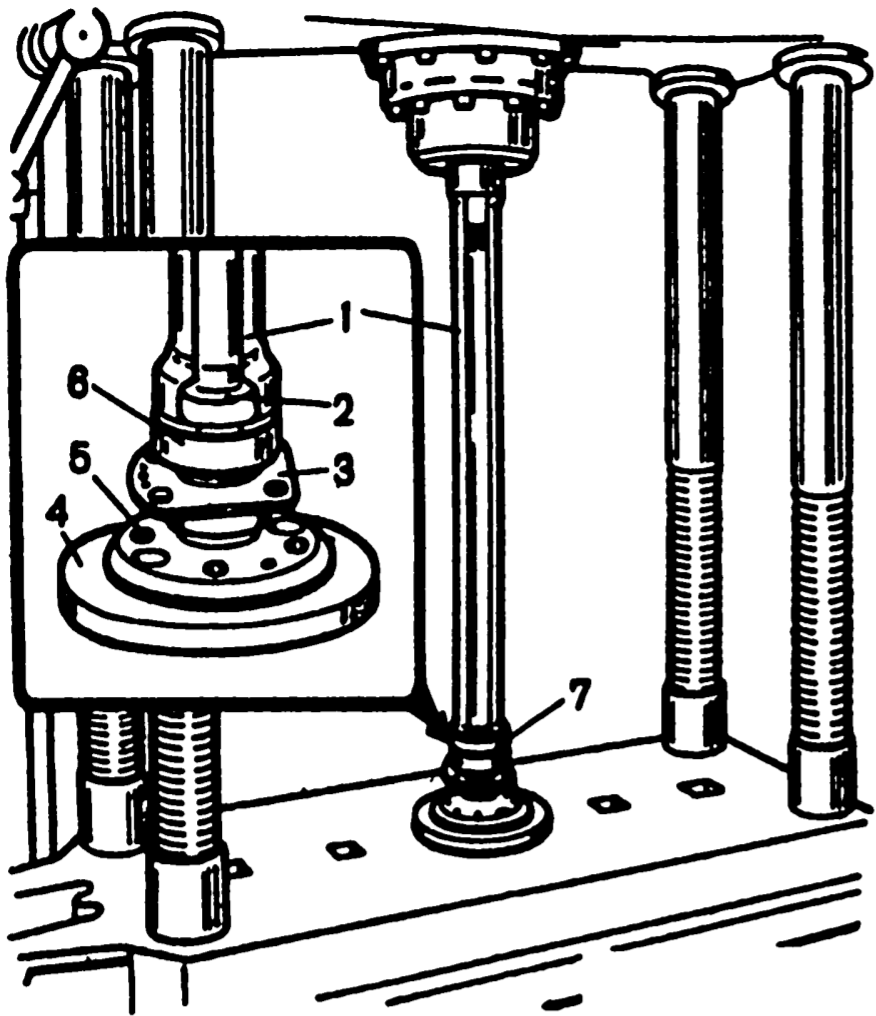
Выпрессовка запорного кольца подшипника полуоси приспособления А.74108/R: 1 - приспособление А.74108/R; 2 - полуось
